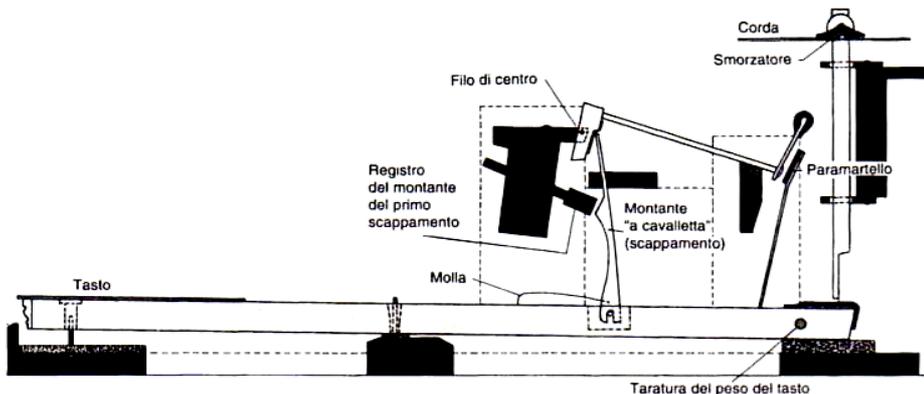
Meccanica di un pianoforte a coda inglese Broadwood del 1799
